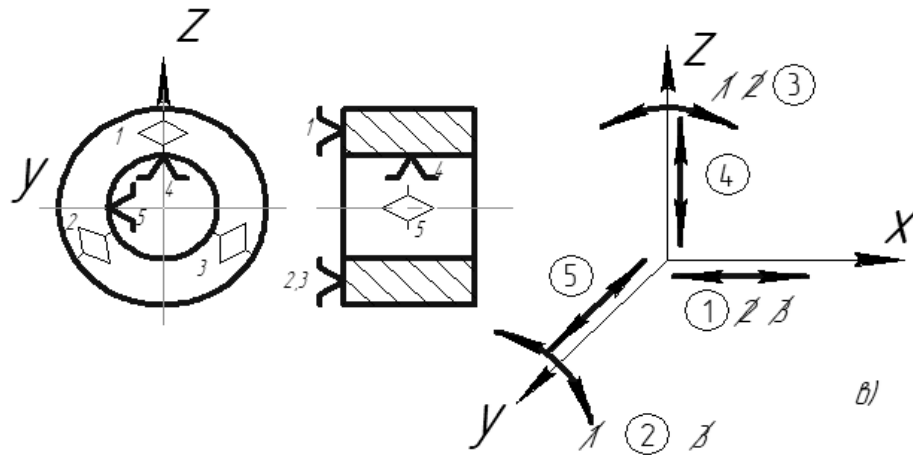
Базування циліндричної заготовки по отвору та торцю
